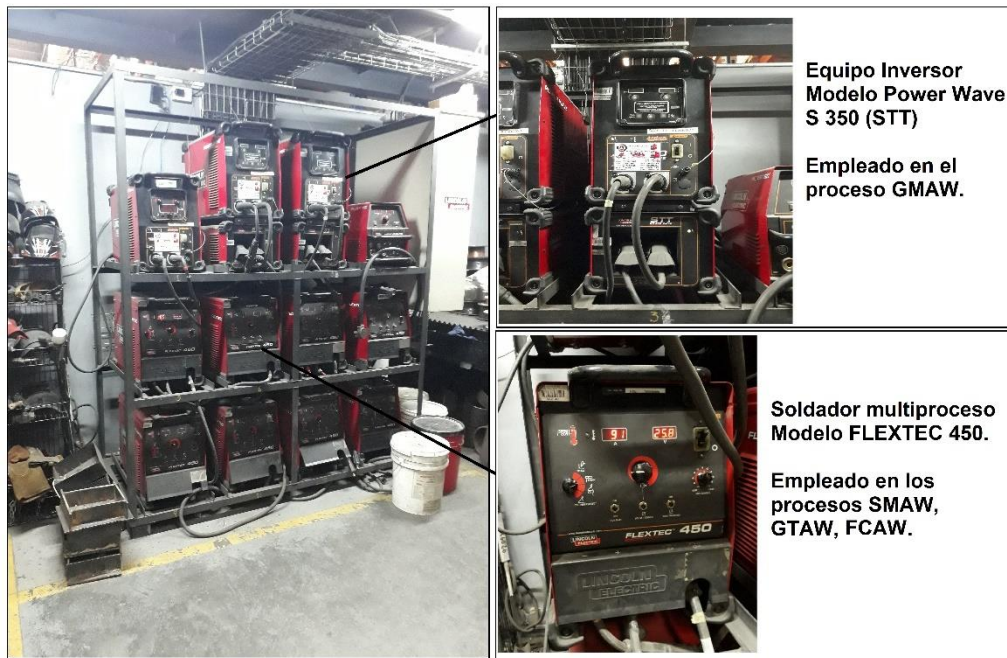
Equipos inversores para realización de soldaduras por procesos SMAW, GTAW, GMAW y FCAW.
